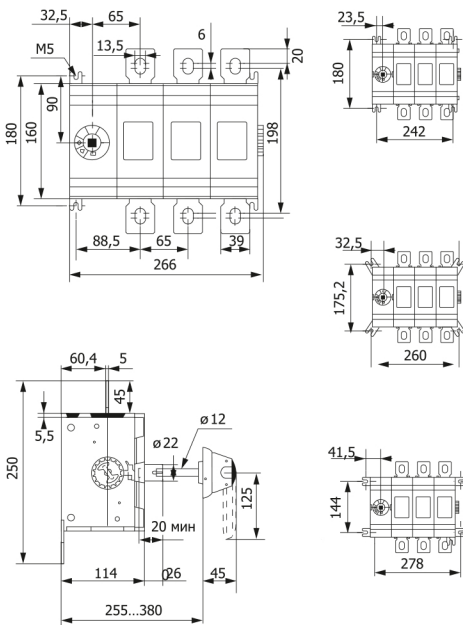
Габаритные и установочные размеры рубильников 600-800А
